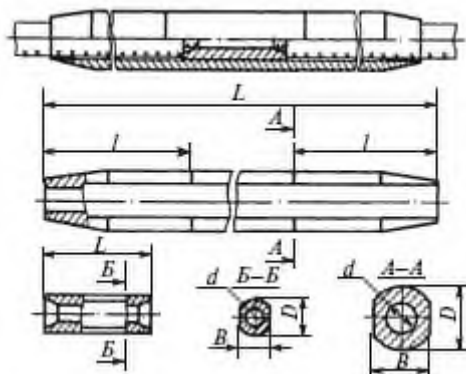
Соединительный прессуемый зажим типа САС для сталеалюминиевых проводов
